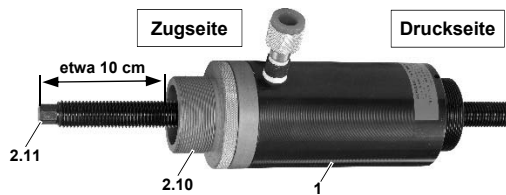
Hydraulik-Zylinder in Grundplatte einschrauben.
